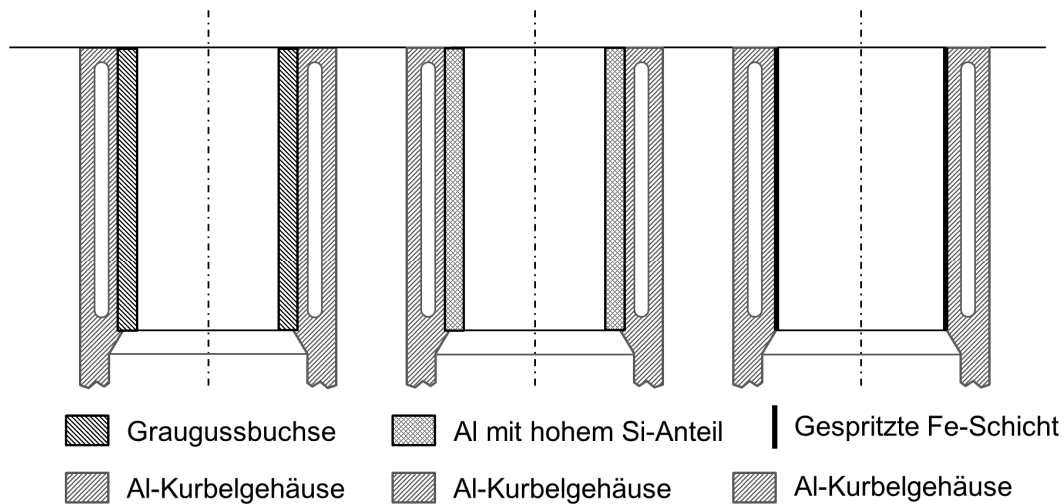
Ausführung der Zylinderwand in Aluminium-Kurbelgehäusen mittels Graugussbuchse, Al-Si Laufbahn sowie gespritzter Eisenschicht
